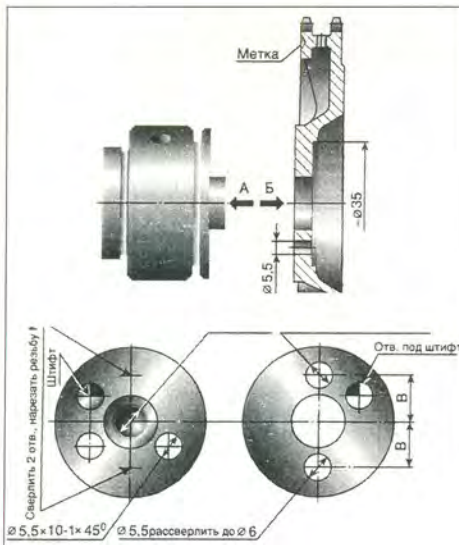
Ремонт (с доработкой) торца распределительного вала (вид А) и звездочки (вид Б).
